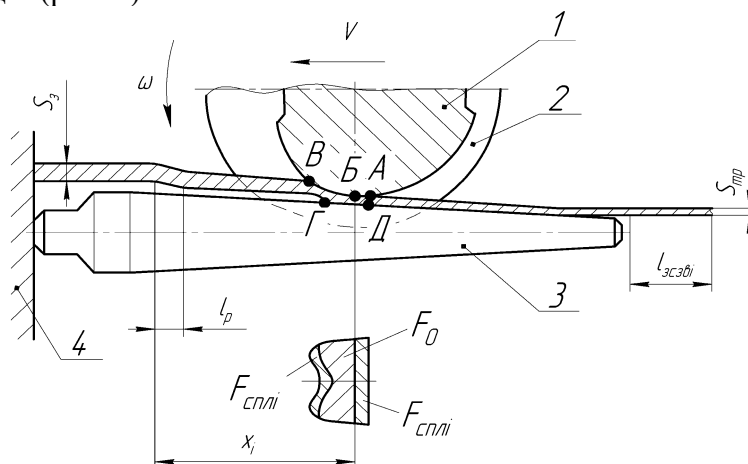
Схема сумарного та миттєвого осередку деформації при деформуванні труби - заготовки зворотним ходом кліті: 1- валок; 2 - рівчак валка; 3 - нерухома оправка; $Sз$ - товщина стінки труби-заготовки; Smp - товщина стінки прокатої труби; АБВГД- миттєвий осередок деформації; V - поступова швидкість валка; ω - кутова швидкість валка; $lзсзві$ - лінійний зсув переднього торця труби; lp - довжина зони редукування; Fo - горизонтальна проекція площі контакту рівчака валка з трубою, що деформується; $Fсплі$ - площа збільшеної частини площі контакту рівчака з трубою за рахунок сплюснення валка; Xi - довжина від початку деформованої труби-заготовки до положення валка і
